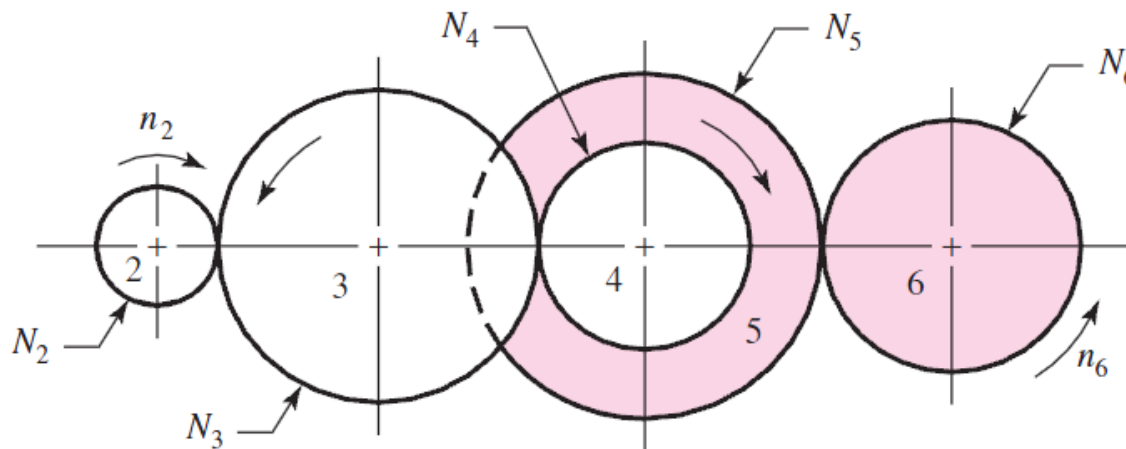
Trem de engrenagens (Shigley, Mechanical Engineering Design, 2011)
